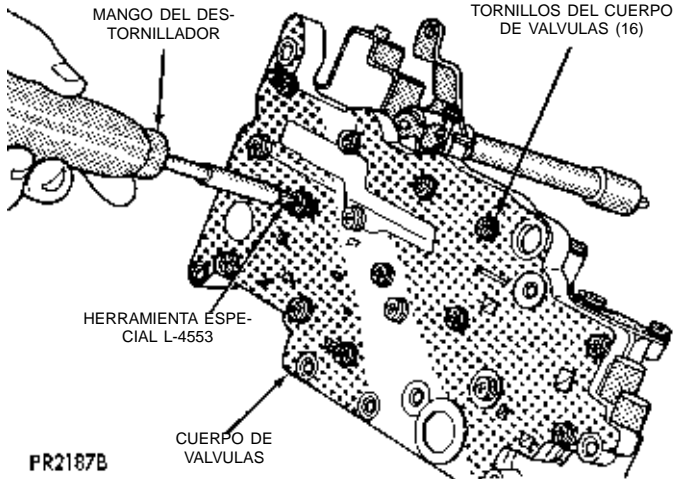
Desmontaje o instalación de los tornillos del cuerpo de válvulas
